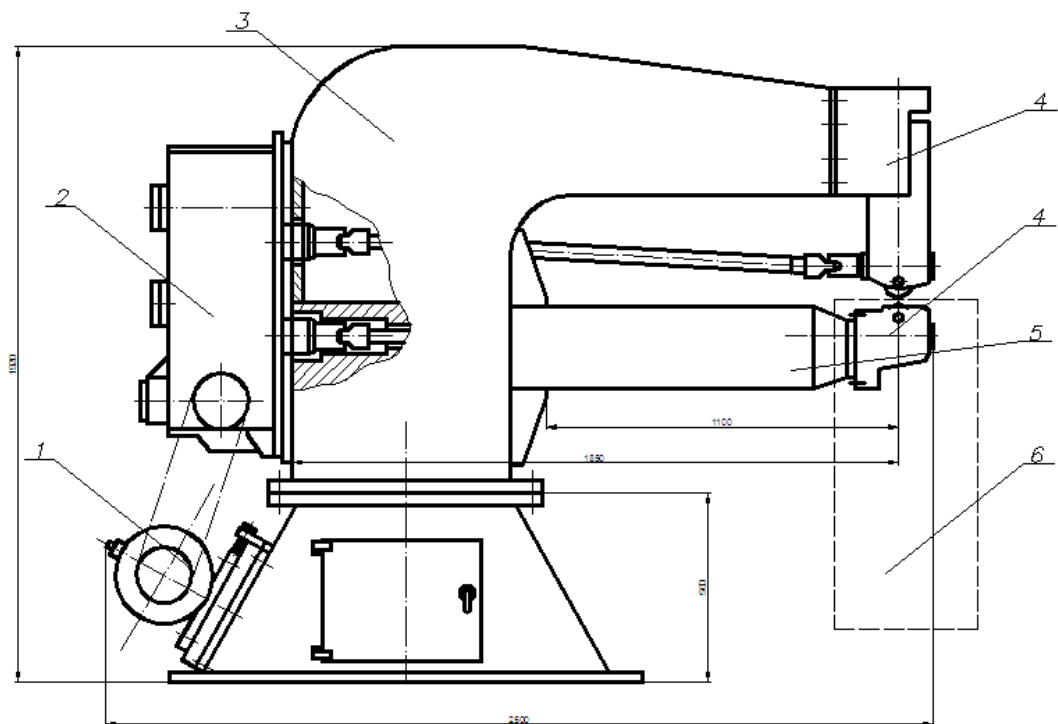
Установа для прокатування повздовжнього шва обичайки зварного бака
